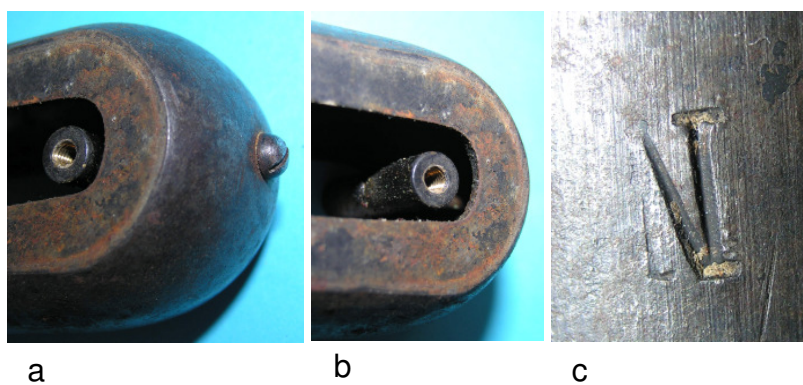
Gewindehülse zur Befestigung der Polückenbleche a und b, Markierung auf dem Magneten
